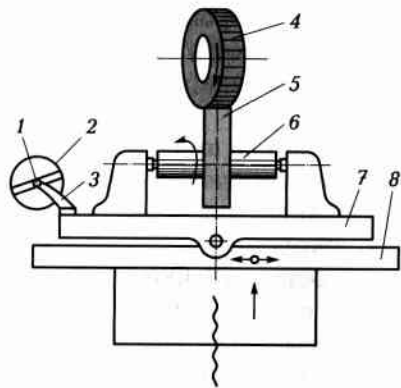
Схема шевингования зубьев зубчатых колес с помощью дискового шевера
